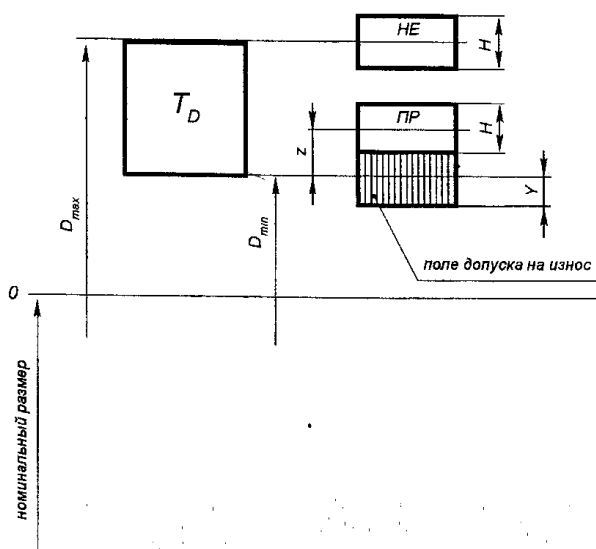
Схема расположения полей допусков калибров для контроля отверстий изготовленных по квалитетам 6, 7 и 8 при номинальных размерах до 180 мм (для размеров отверстий изготовленных по квалитетам от 9 до 17,  $Y = 0$ )
